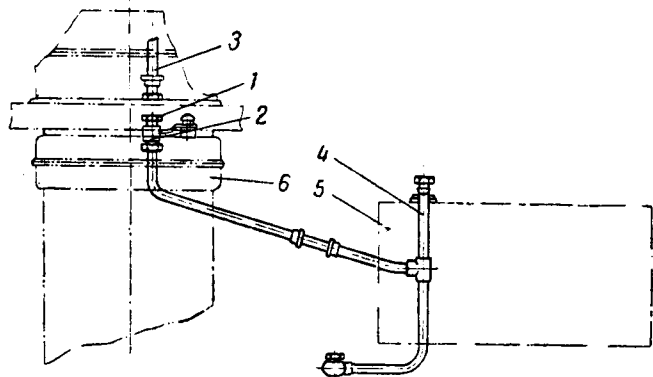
Схема для заливки разжижителя через дренажную трубку масляного бака:
